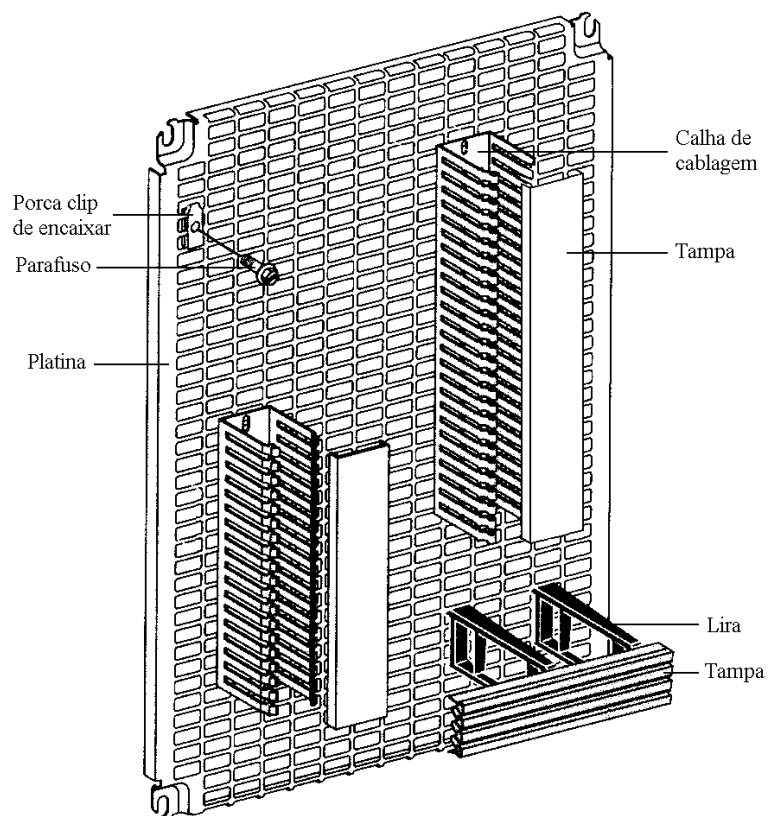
Liras e calhas de cablagem instaladas em platina.
